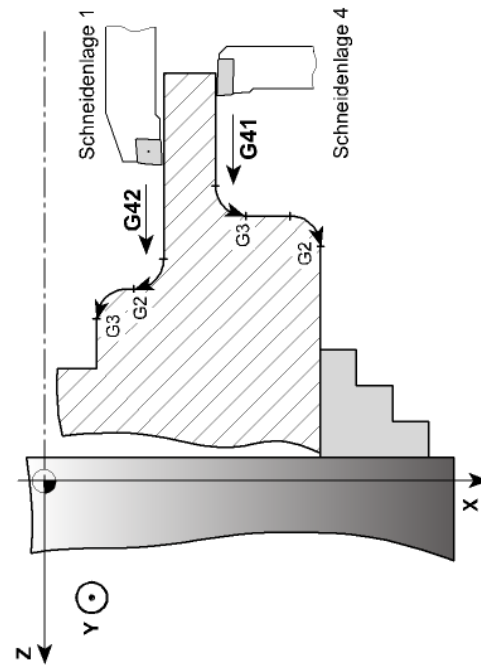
Werkzeugbahn-Korrektur G41, G42 bei Bearbeitung hinter und vor
